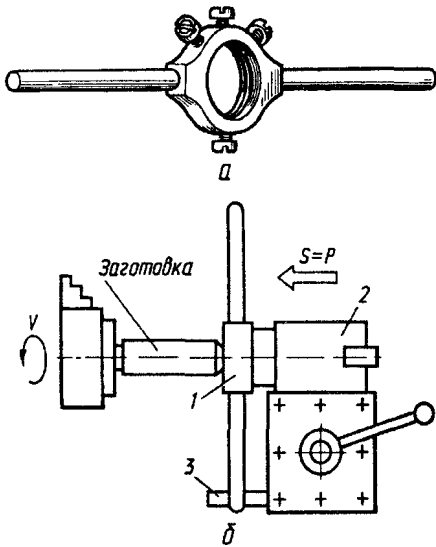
Нарізування різьби плашкою: а - плашкотримач-вороток; б - застосування упорної планки; 1 – плашкотримач; 2 - упор; 3- планка
